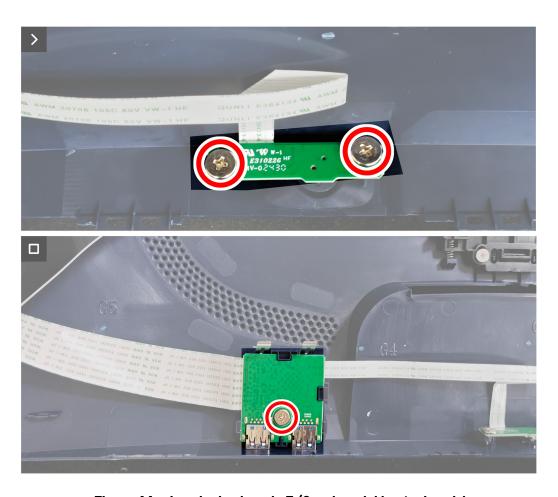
Instalar la placa de E/S y placa del botón Joystick
